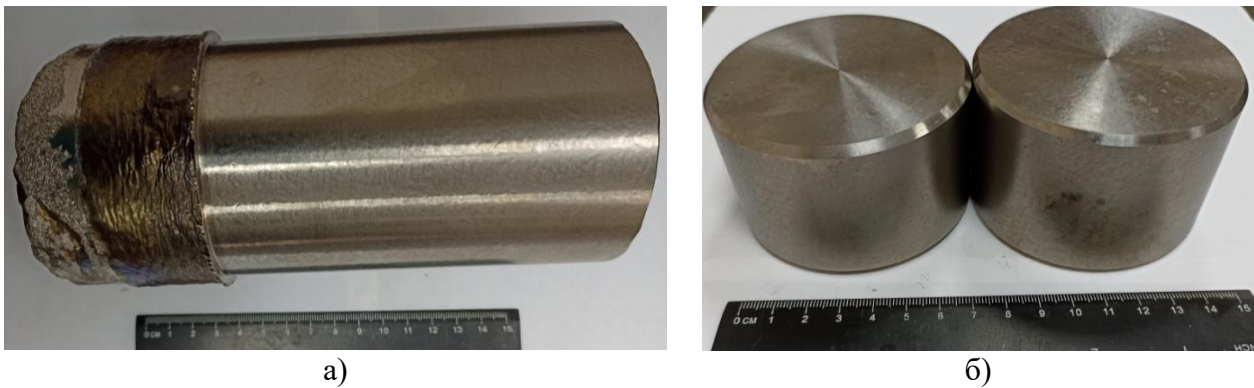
Дослідний електрошлаковий зливкок вторинного титану та зразки для кування: а) електрошлаковий зливкок вторинного титану після обточування альфірованого шару; б) зразки для гарячого кування
